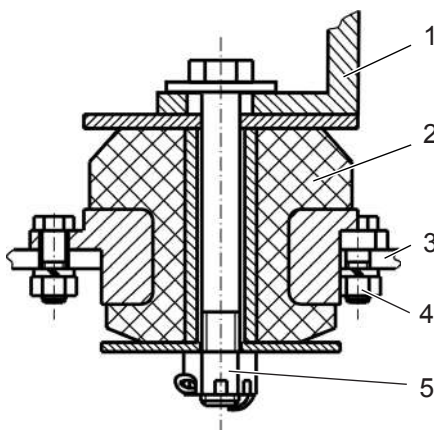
Опора силового агрегата с двигателем Daimler, Weichai
